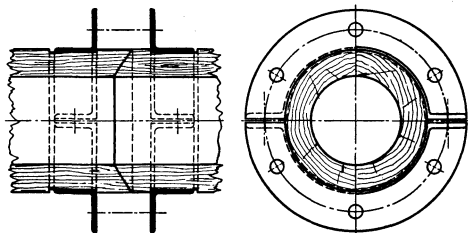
Holzrohrverbindung mit Flanschen (Kleinholz-Weber).
